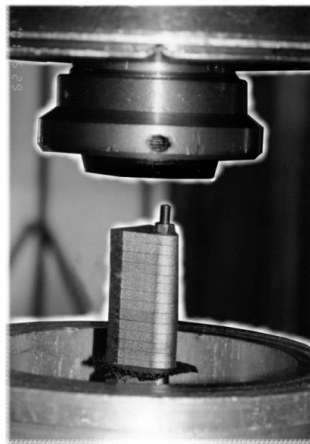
Робоча зона верстата «Дуга-8» при обробці пакета деталей
